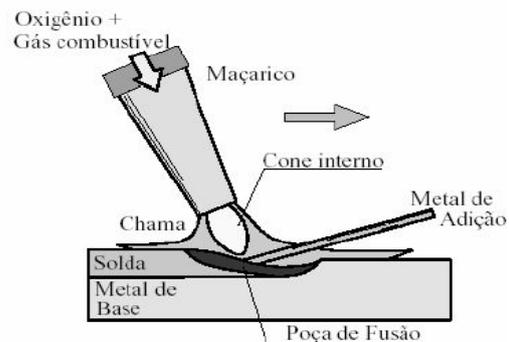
Soldadura oxiacetilénica. Fonte - Altino Loureiro
